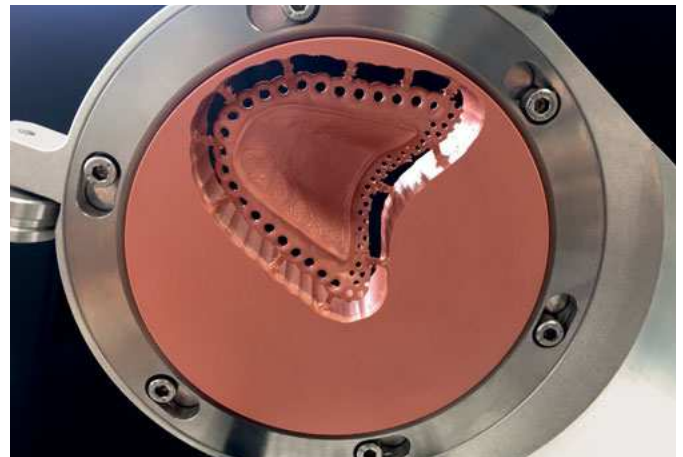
Fertig gefräste Oberkiefergaumenplatte.
